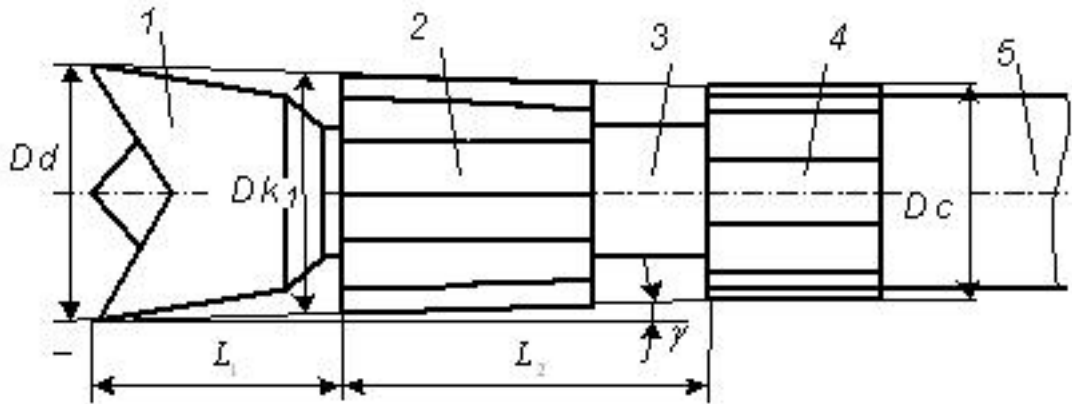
Компоновка с коническим калибратором 1 - долото, 2 - конический калибратор, 3 - вал забойного двигателя, 4 - центратор, 5 - шпиндель ЗД
